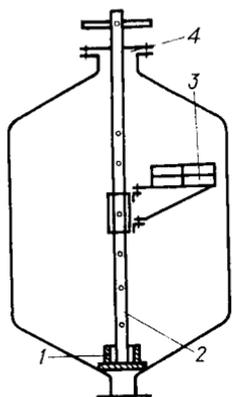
Люлька для сварки внутренних швов аппарата:
